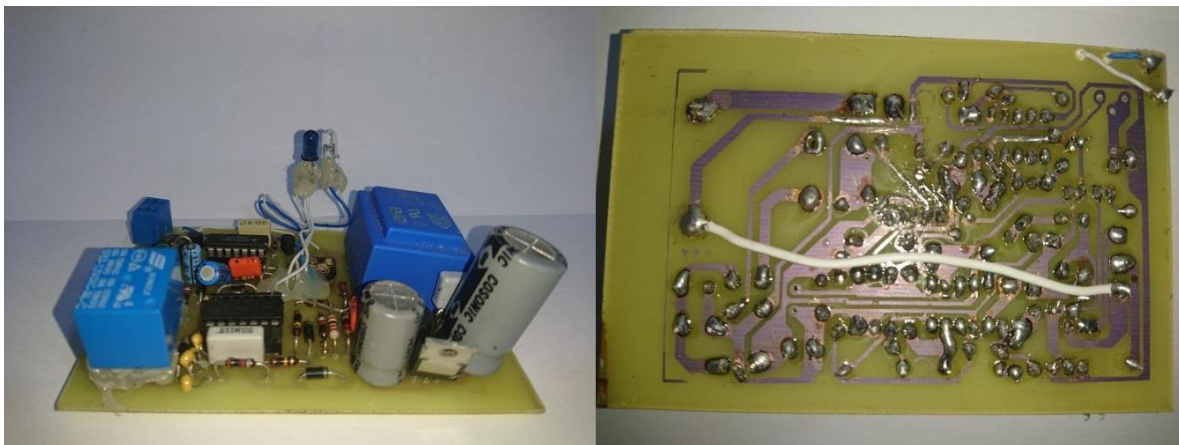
Photo des deux faces de la carte après soudage des composants.
